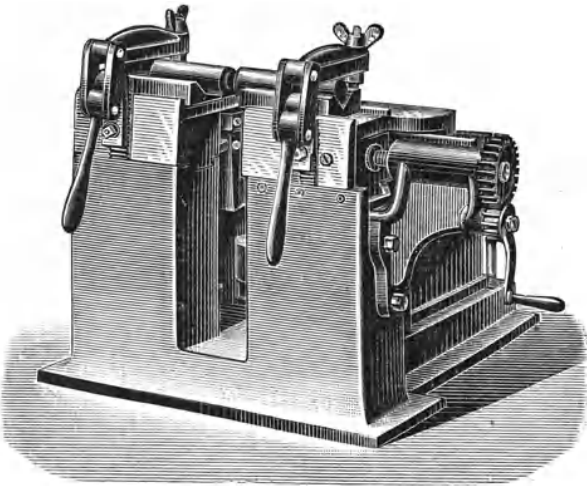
Schweißapparat für stärkere Stücke.
